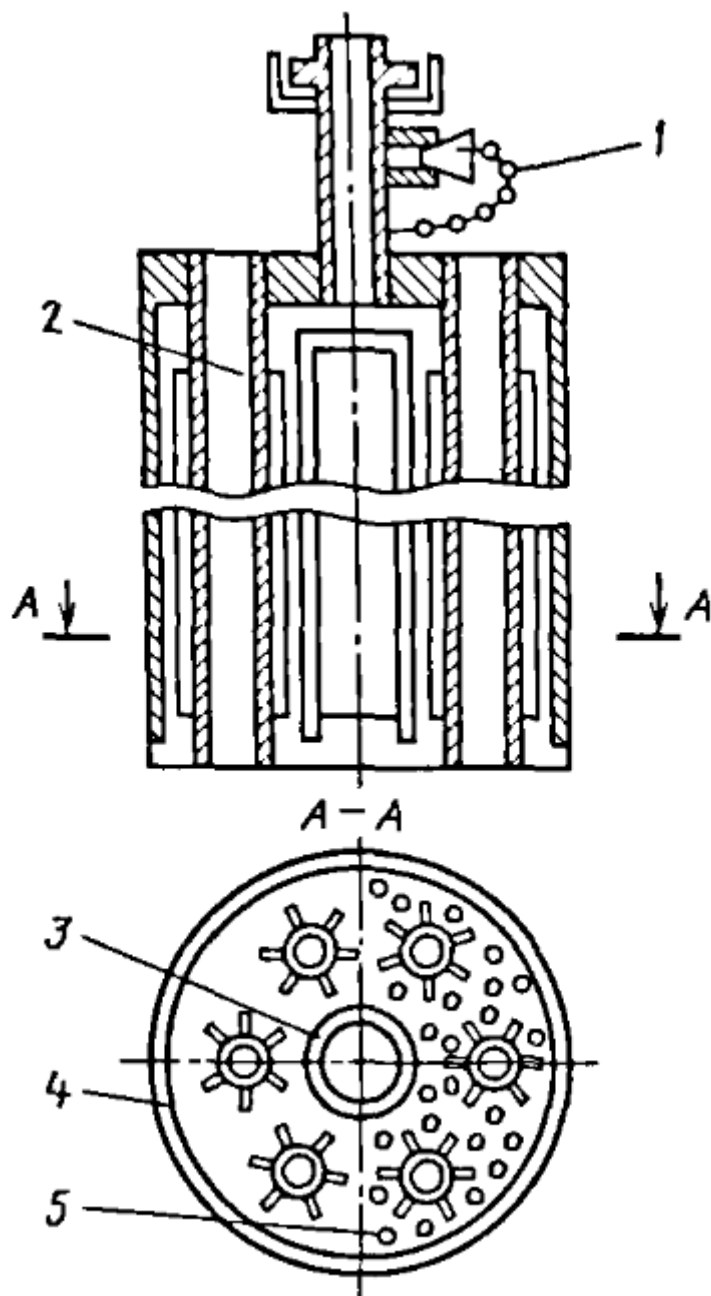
Погружной адсорбционный насос с медными рёбрами. 1 – заглушка; 2 – дополнительные охлаждающие трубки; 3 – внутренний цилиндр для подвода газа; 4 – корпус; 5 – адсорбент [4, с. 514]
